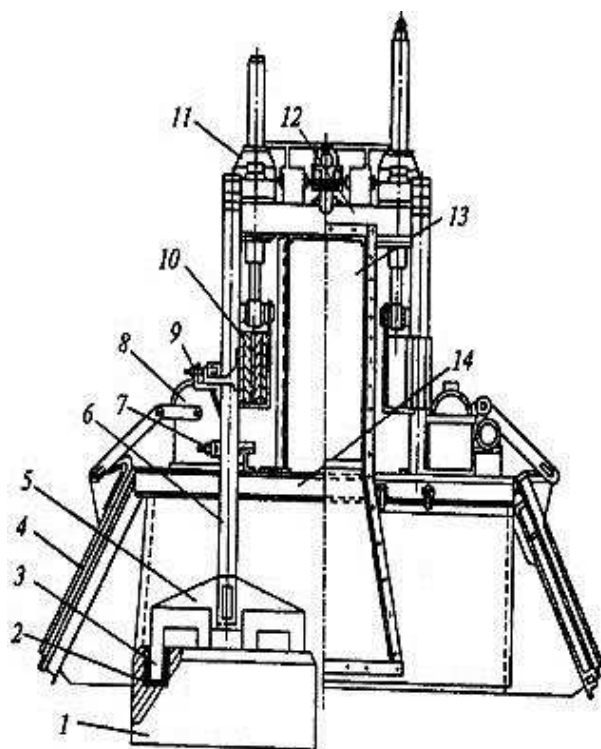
Анодное устройство: 1-анодный блок; 2- ниппель; 3-кронштейн; 4-сварочное соединение; 5-штанга;
